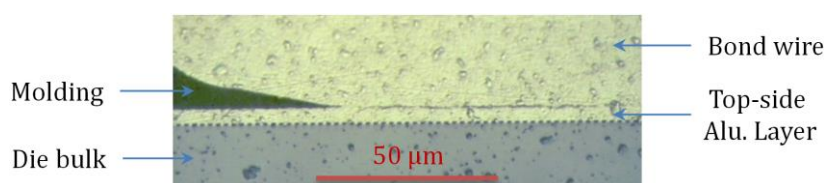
fissure au pied d'un fil de bonding connectant la source d'une puce en boîtier conventionnel après vieillissement par cyclage thermique.
